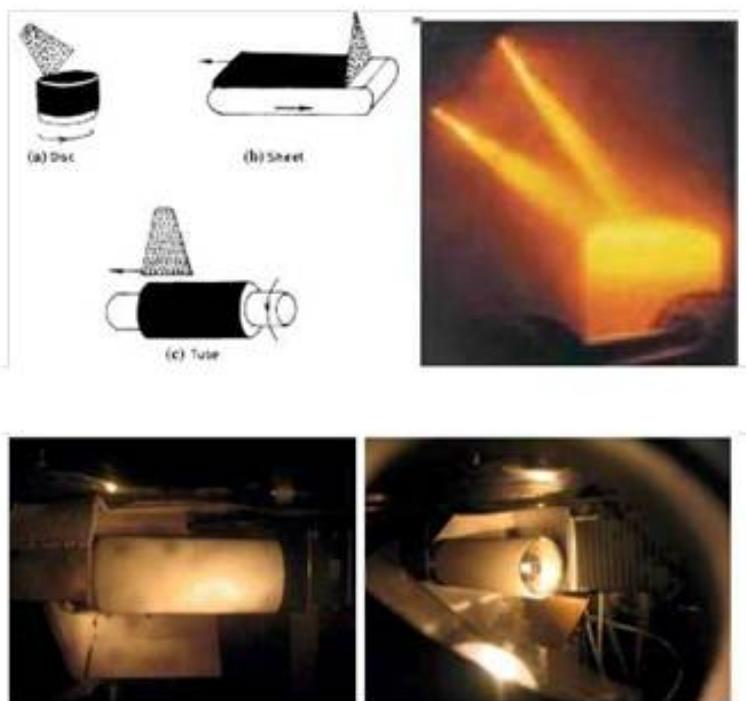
Схемы технологии Spray forming для получения цилиндрической заготовки (болванки)
